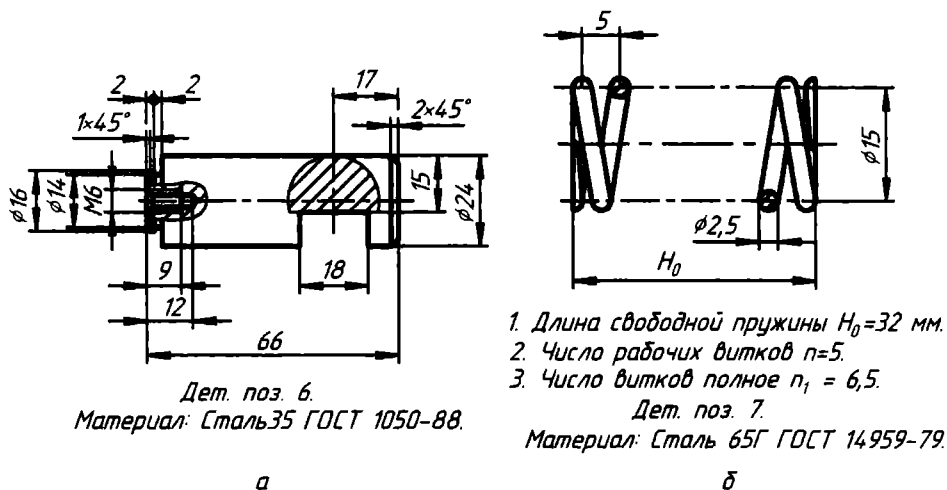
Чертежи: а — ползуна; б — пружины
